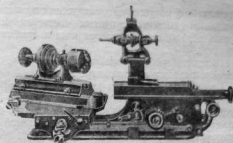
Настольный круглошлифовальный станок Дикси для наружной шлифовки.
